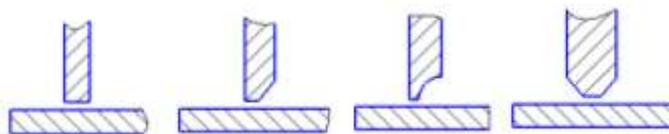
Форма подготовленных кромок под сварку для тавровых соединений [20].
